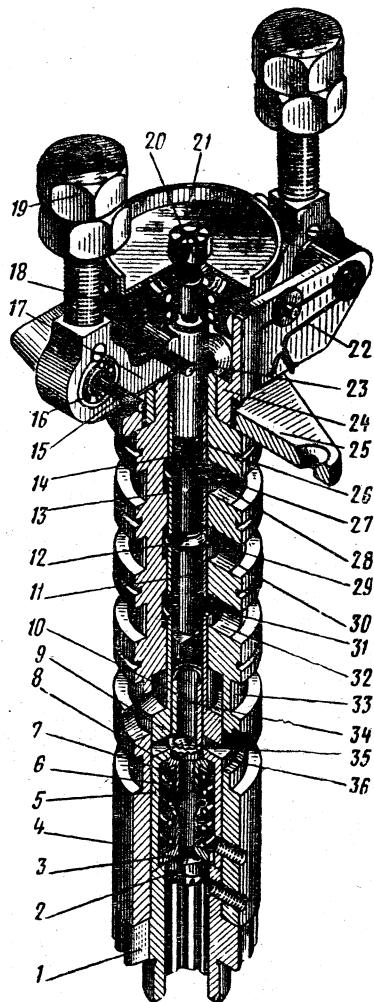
Золотниковая часть регулятора числа оборотов вала дизеля 2Д50:
